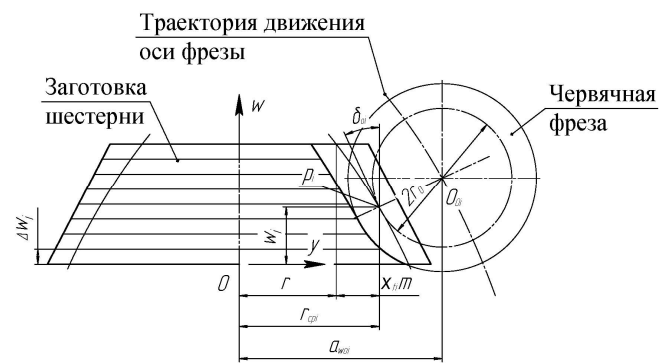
Схема формирования зубьев конической шестерни червячной фрезой
